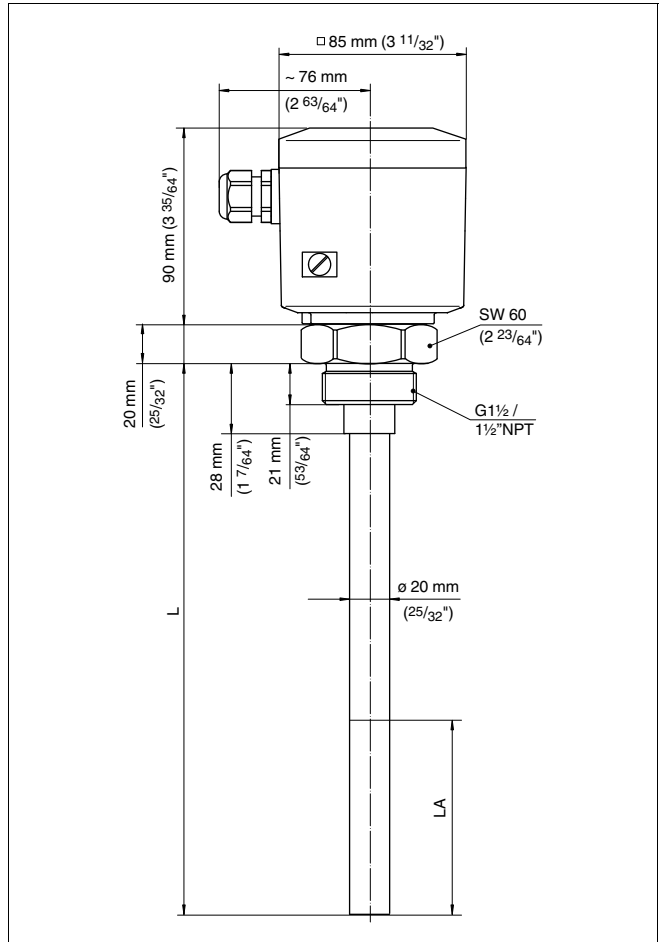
VEGACAP 27, Gewindeausführung G1½ A
